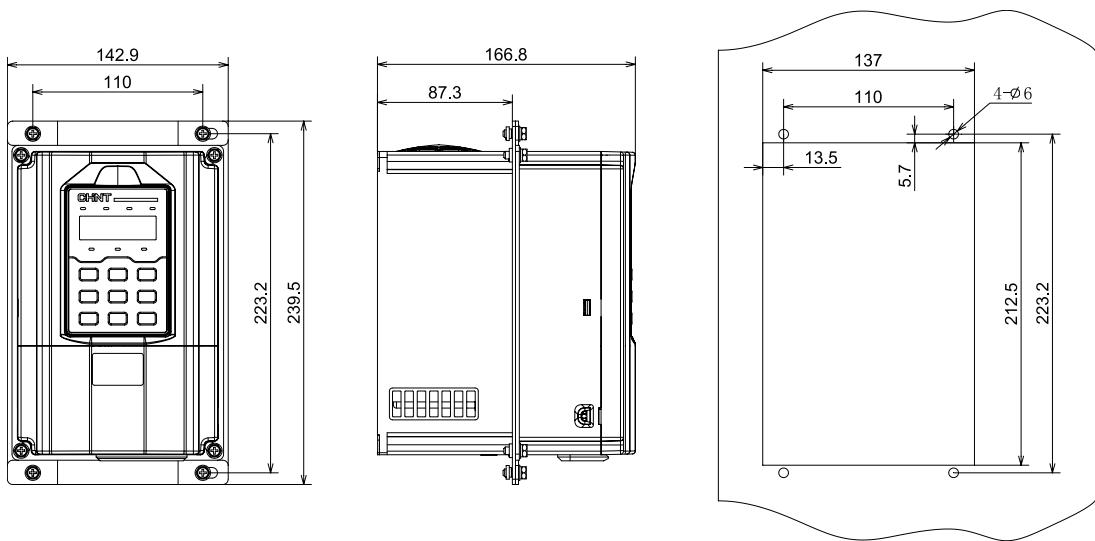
Комплект фланцевого монтажа для типоразмера Т2
